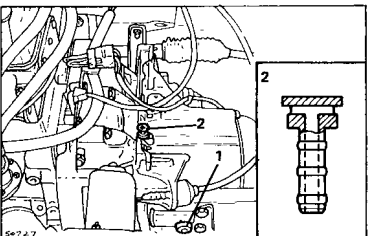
Расположение пробки маслониливного отверстия коробки передач (поздние типы)
